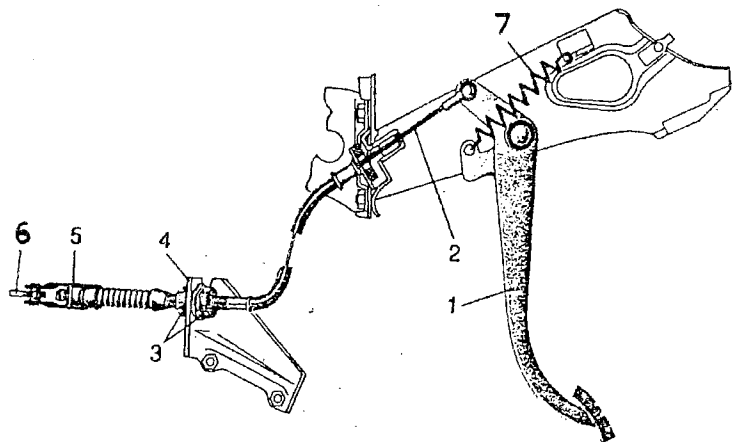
Тросовый безззорный привод выключения сцепления:
